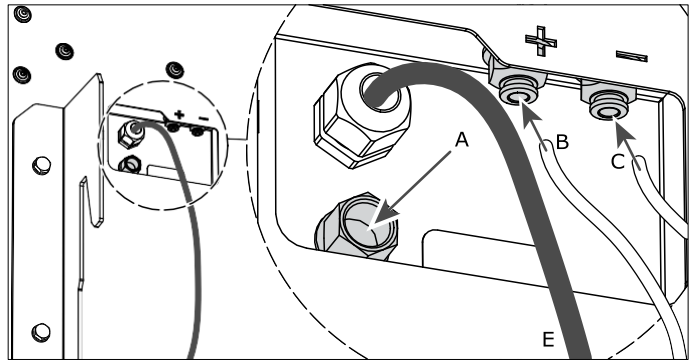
Collegamento dell'aria compressa (parte posteriore dell'unità)
